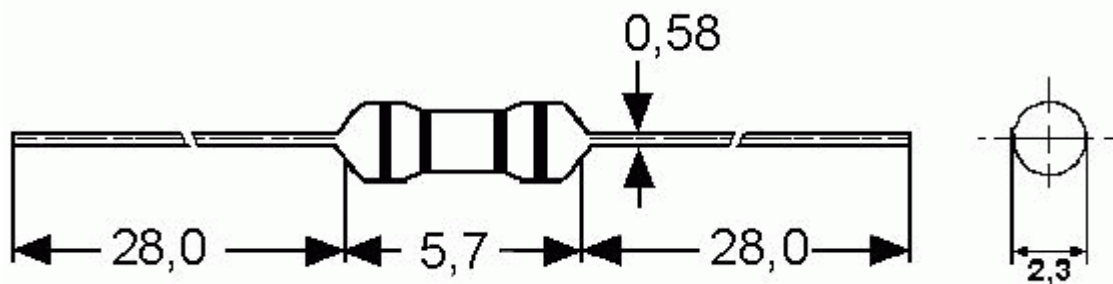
Габаритні розміри резистора типу MF-0.125
